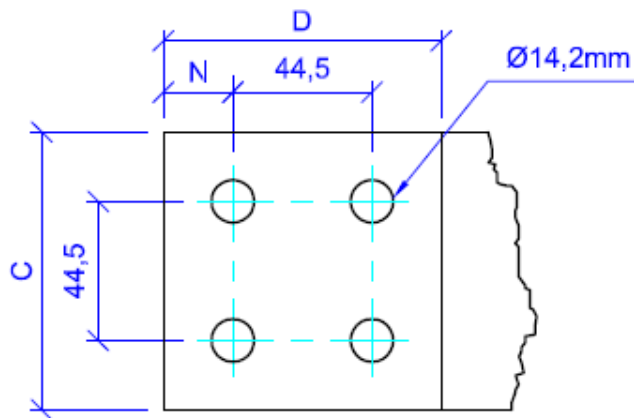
Conector Terminal 90° Cabo-Chapa – 4 Furos
